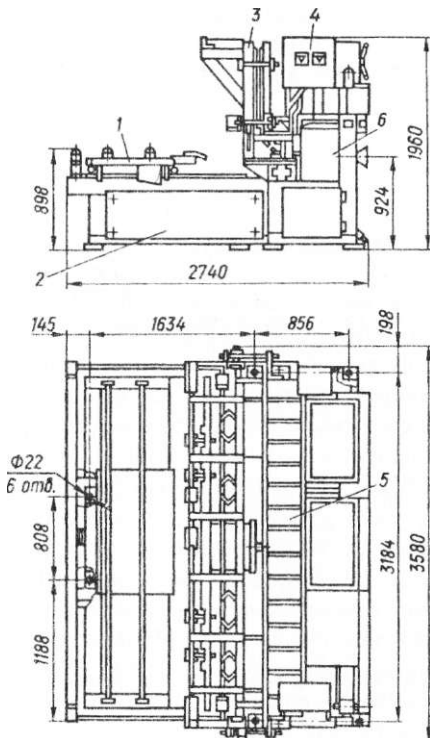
Зовнішній вигляд машини для багатоточкового зварювання арматурних сіток МТМ-32УХЛ4:
